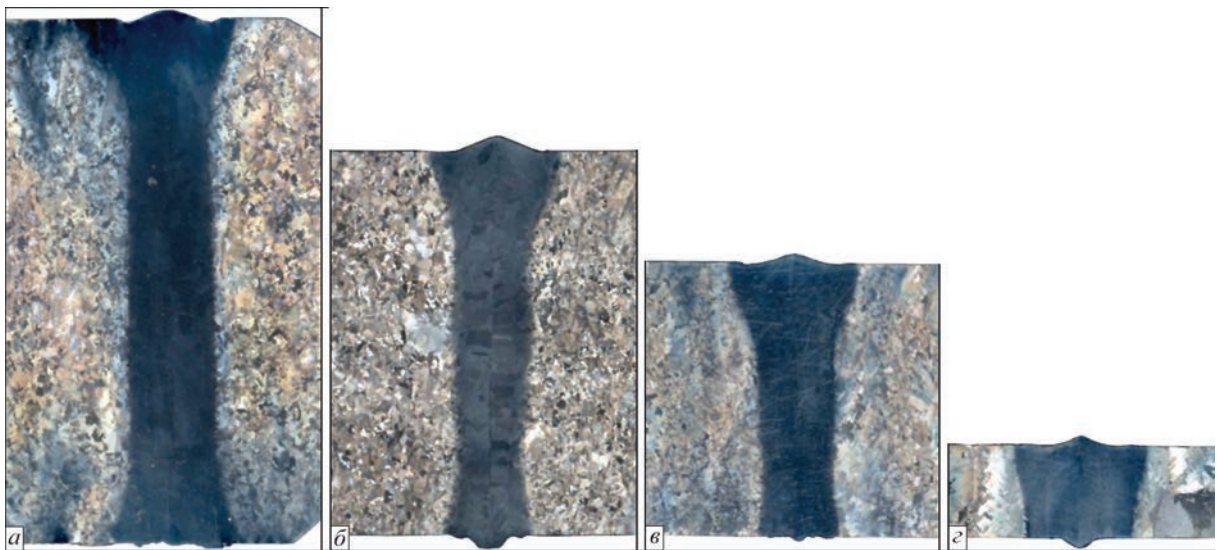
Макроструктура сварных соединений литейного сплава ВТ5Л1 различной толщины при ЭЛС со сквозным проплавлением: а — $\delta_{св} = 26$ мм; б — 17; в — 14; г — 5
